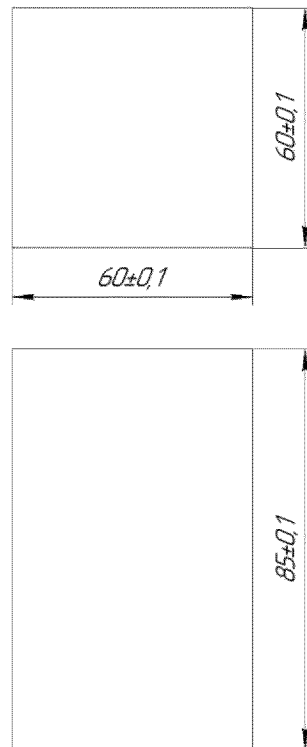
Ескіз заготовки, отриманої з прокату сортового сталевих гарячекатаного квадратного
